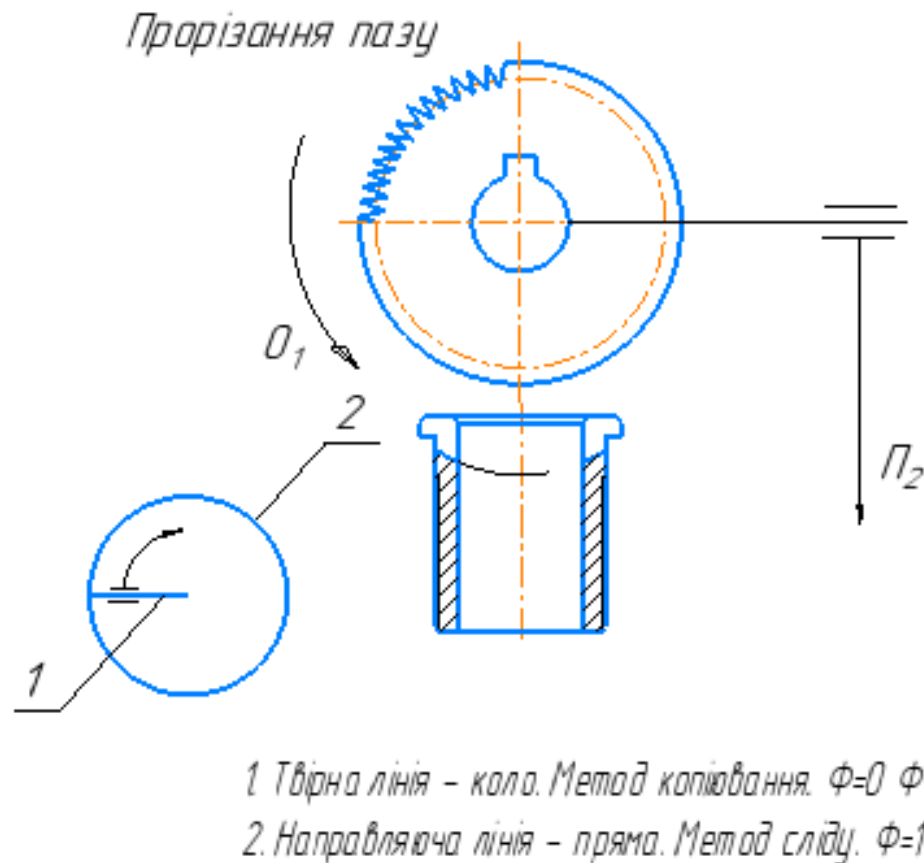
Формоутворюючі рухи при прорізанні пазу дисковою фрезою
